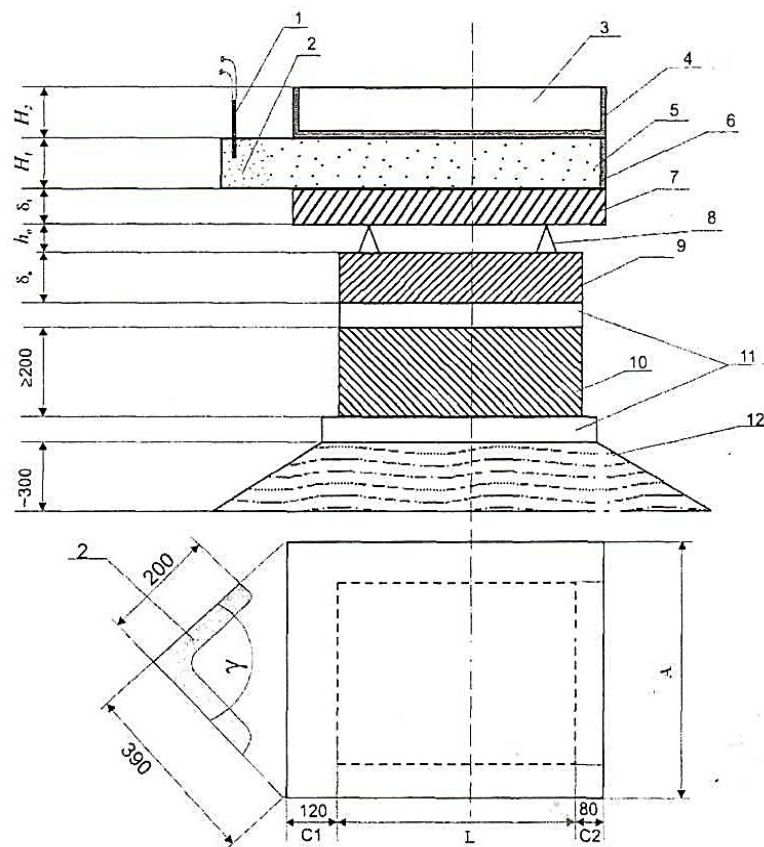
Схема установки свариваемых заготовок и заряда взрывчатого вещества при изготовлении плакированных заготовок
